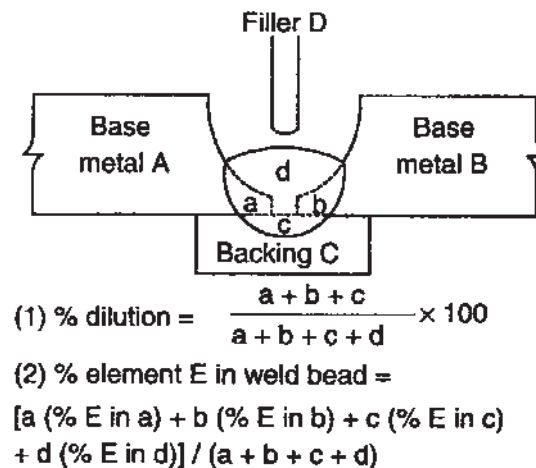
Dilución y composición del metal de aporte en la soldadura de dos materiales disímiles⁶.
